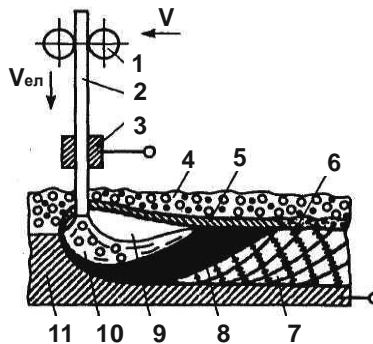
Схема автоматичного дугового зварювання під флюсом:
